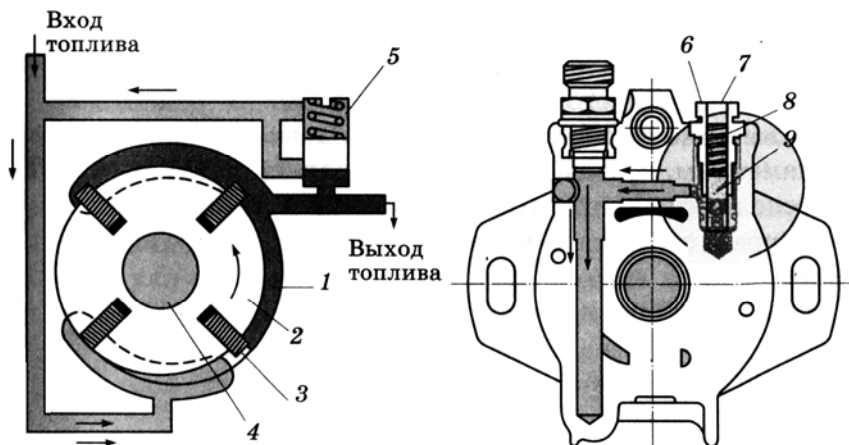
Топливный насос низкого давления и регулирующий клапан:
